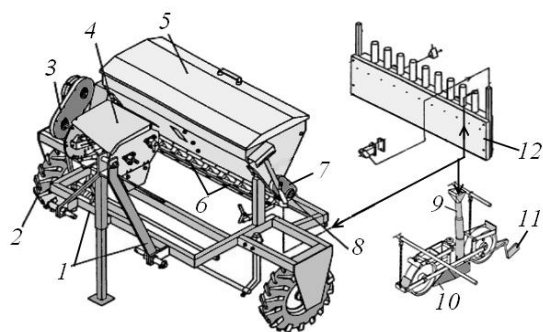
Общее устройство лесопитомниковой сеялки: 1 – рама с навеской; 2 – опорно-приводное колесо; 3 – цепная передача; 4 – многоступенчатый редуктор с 20-ю передачами; 5 – бункер для семян; 6 – катушечный высеваящий аппарат; 7 – цепная передача привода ворошилки семян; 8 – вал высеваящего аппарата; 9 – семяпровод; 10 – сошник; 11 – заделывающее устройство; 12 – приставка для сплошного посева семян
